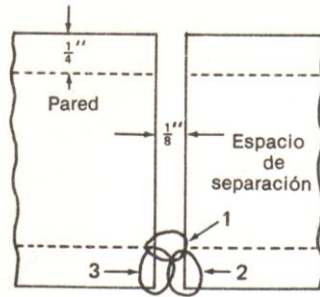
Termino de la soldadura con dos pasadas más.
